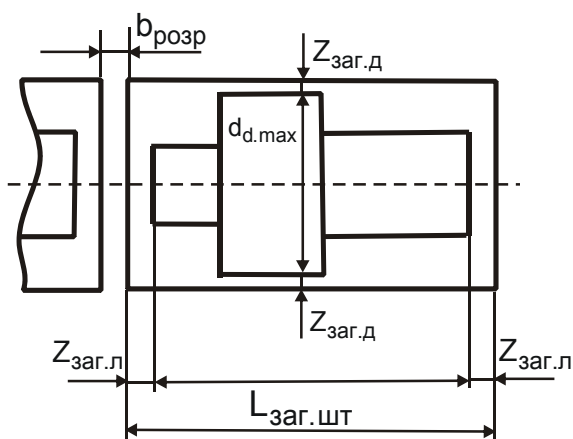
Ескіз заготовки із круглого прокату для деталі типу “вал східчастий”
